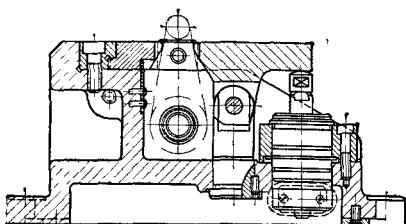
Рычажное приспособление для фрезерования паза в вилке
